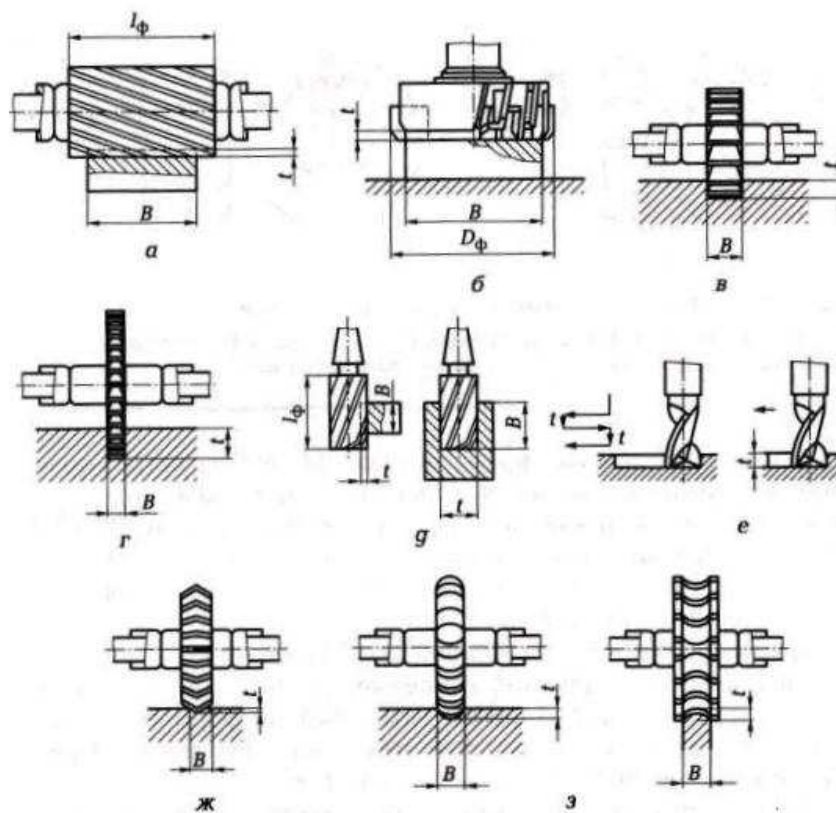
Схемы фрезерования цилиндрическими (а), торцовыми (б), дисковыми (в), прорезными (г), концевыми (д), ипоночными (е), угловыми (ж) и фасонными (з) фрезами: B — ширина фрезерования; t — глубина фрезерования; D_ϕ — диаметр фрезы; l_ϕ — длина режущей части фрезы
